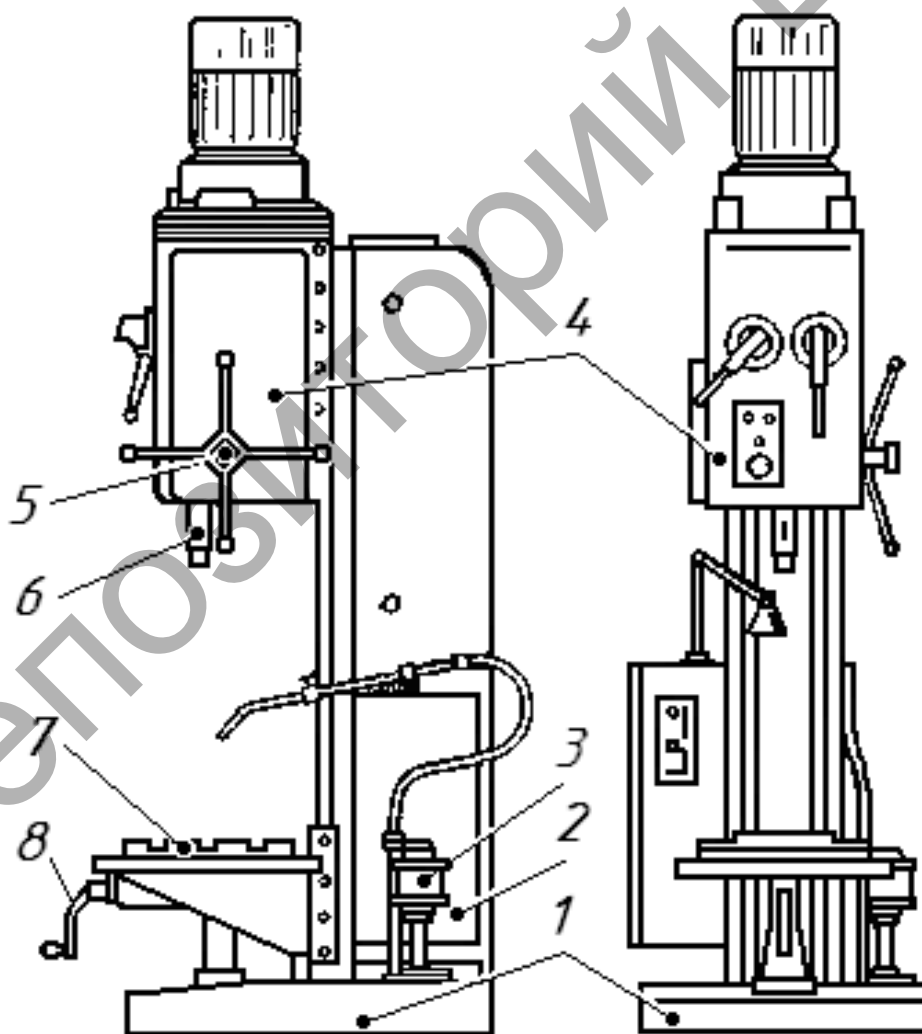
Станок вертикально-сверлильный модели 2Н118
